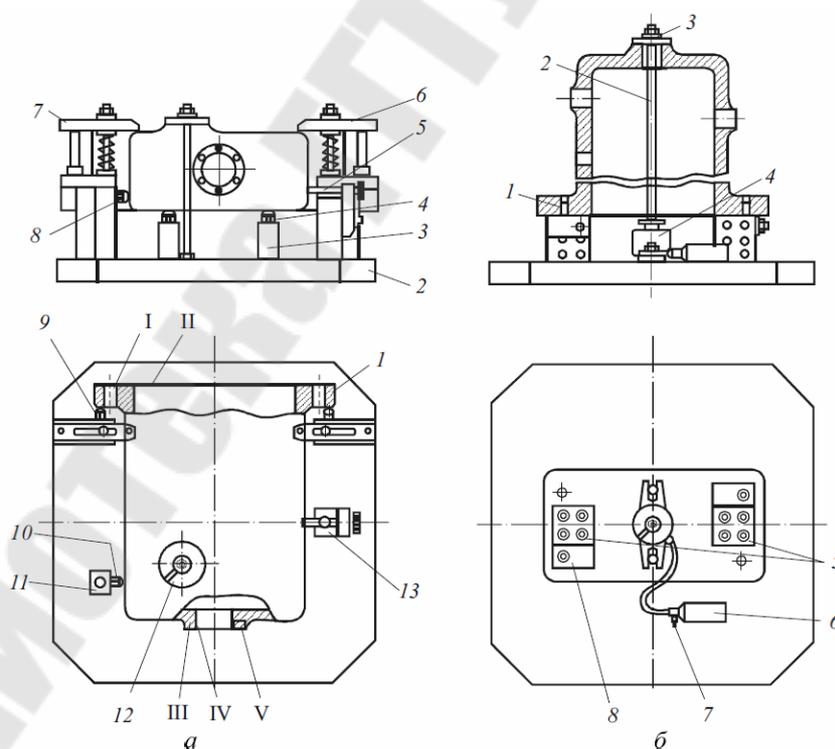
Компоновка приспособлений для обработки корпуса с шести сторон за два установка [4]
